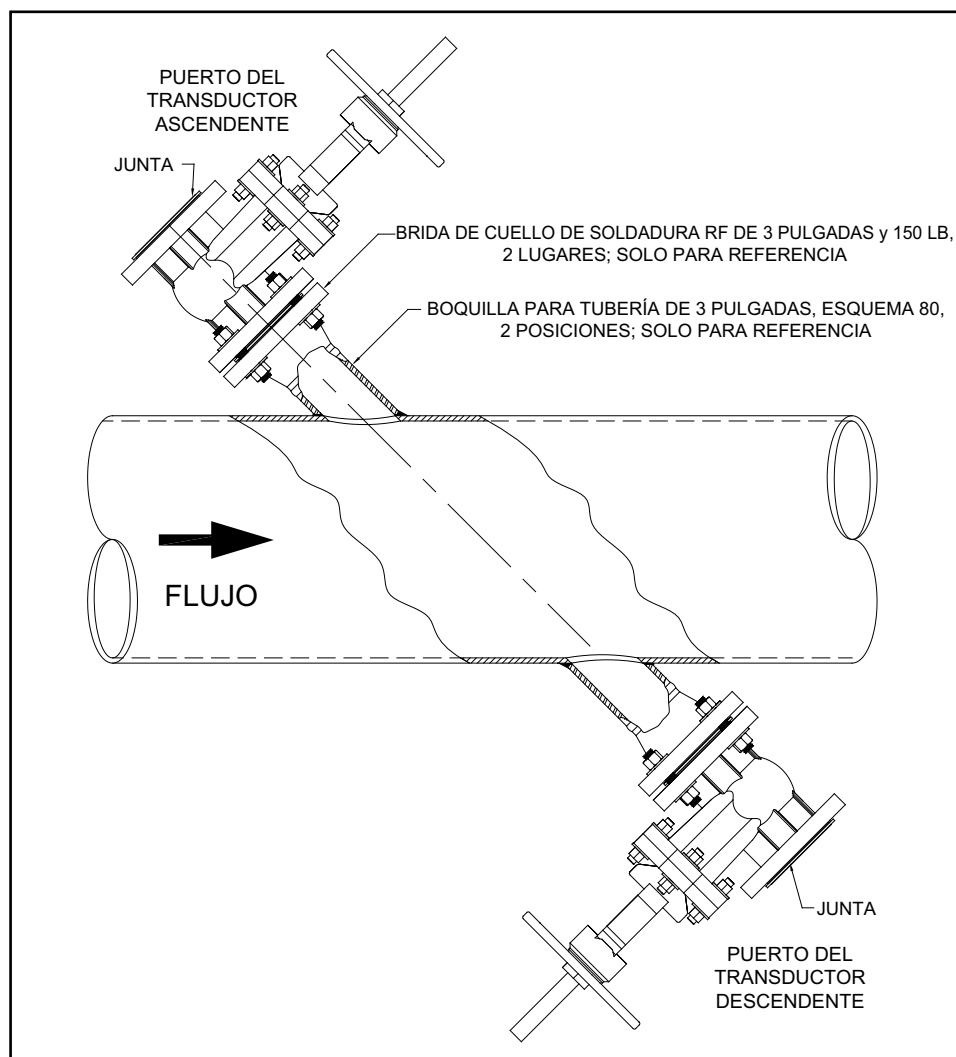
Instalación de válvulas de aislamiento - Conjunto estándar
